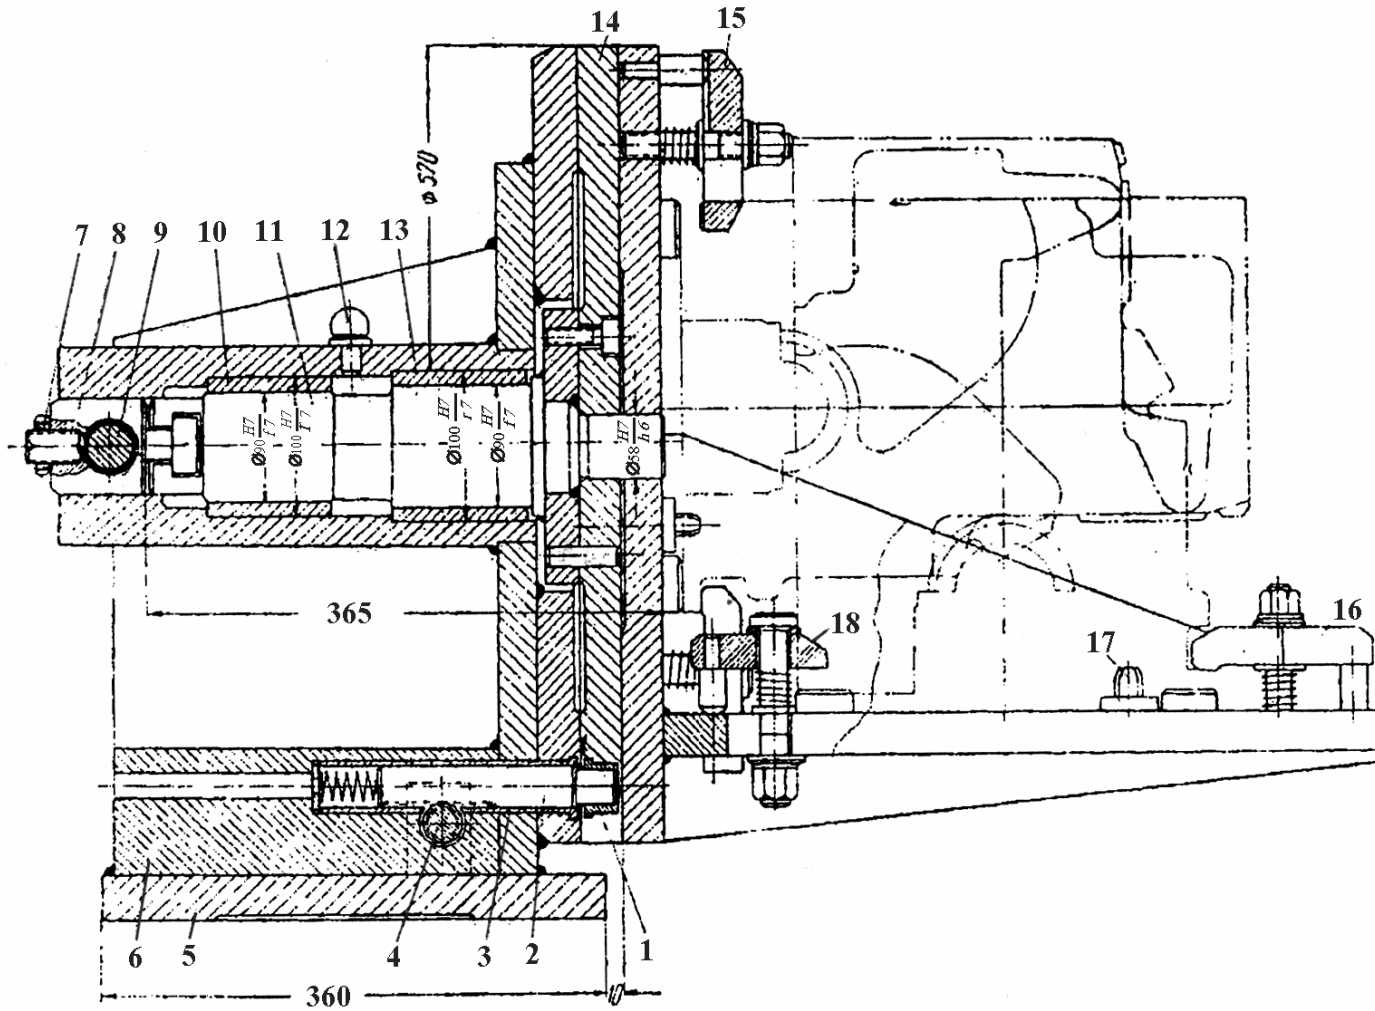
Поворотний стэнд для кріплення блока циліндрів при ремонті:
